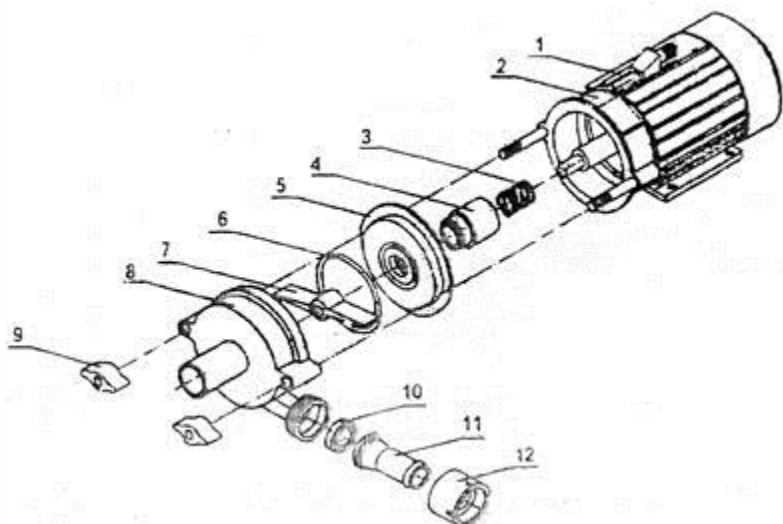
Молочный насос НМУ-6: 1- электродвигатель; 2 – фланец; 3 – пружина; 4 – уплотнитель наконечника; 5 – стенка; 6 – кольцо уплотнительное; 7 – крыльчатка; 8 – корпус; 9 – гайки; 10 – клапан обратный; 11 – патрубок нагнетательный; 12 – гайка.
